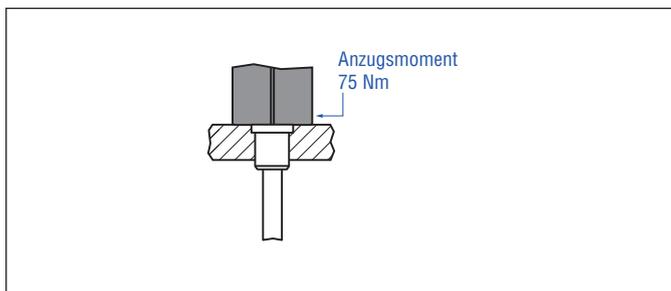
Einbaubeispiel für Gewindeflansch »F«, »M«, »S«, »W«
